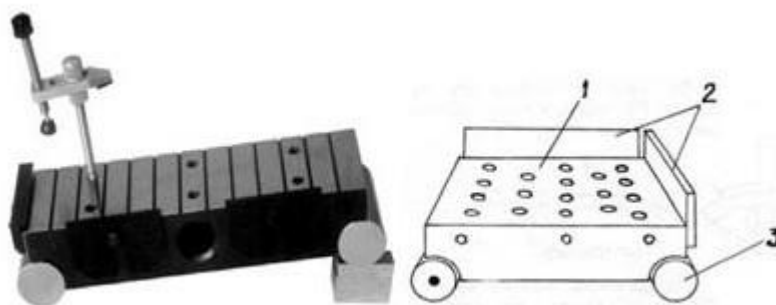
Лінійка синусна (1 - стіл; 2 - планки опорні; 3 - кулька)
